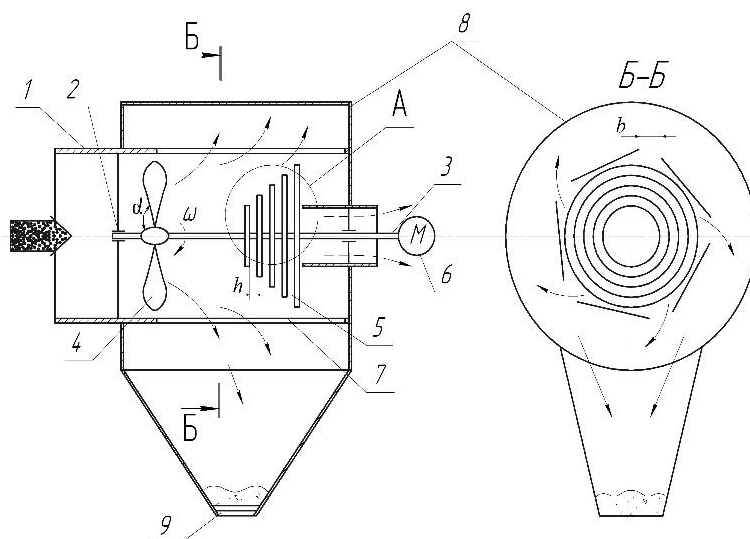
Конструктивная схема разработанного циклона с многодисковым доочистителем: 1 - цилиндрический корпус; 2 - опоры; 3 - вал; 4 - завихритель; 5 - многодисковый доочиститель; 6 - электродвигатель; 7 - жалюзи; 8 - пылесадочная камера; 9 - шлюзовой затвор; - движение запылённого воздушного потока; - дисперсных частиц; - очищенного воздушного потока.
